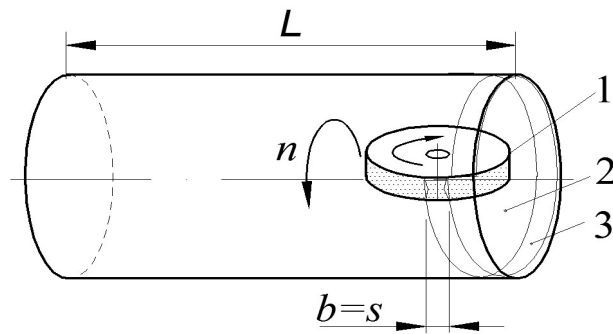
Схема обработки внутренней поверхности цилиндра:
